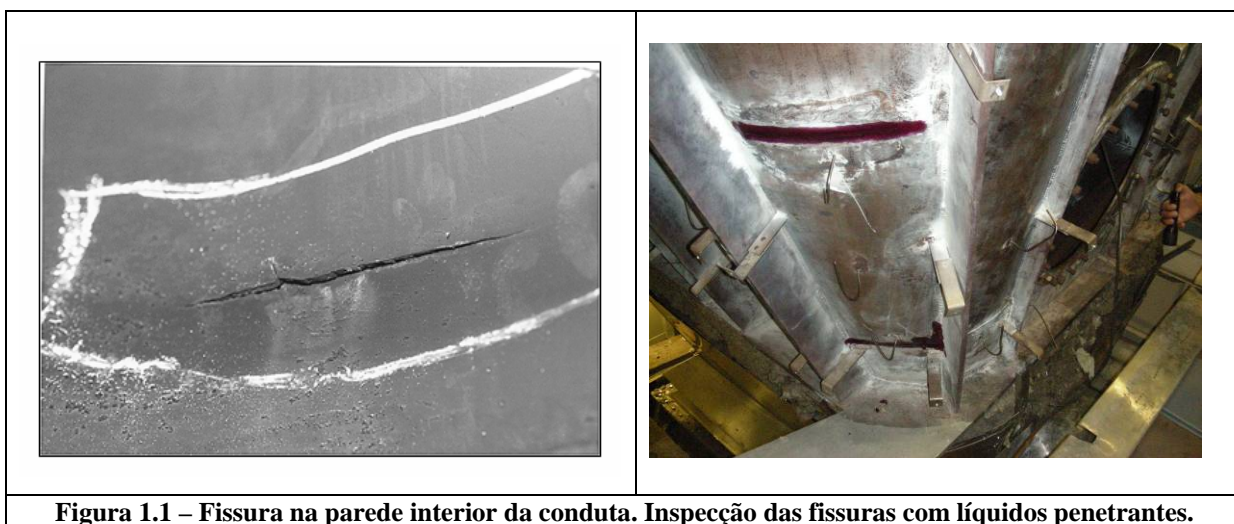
Fissura na parede interior da conduta. Inspeção das fissuras com líquidos penetrantes.
